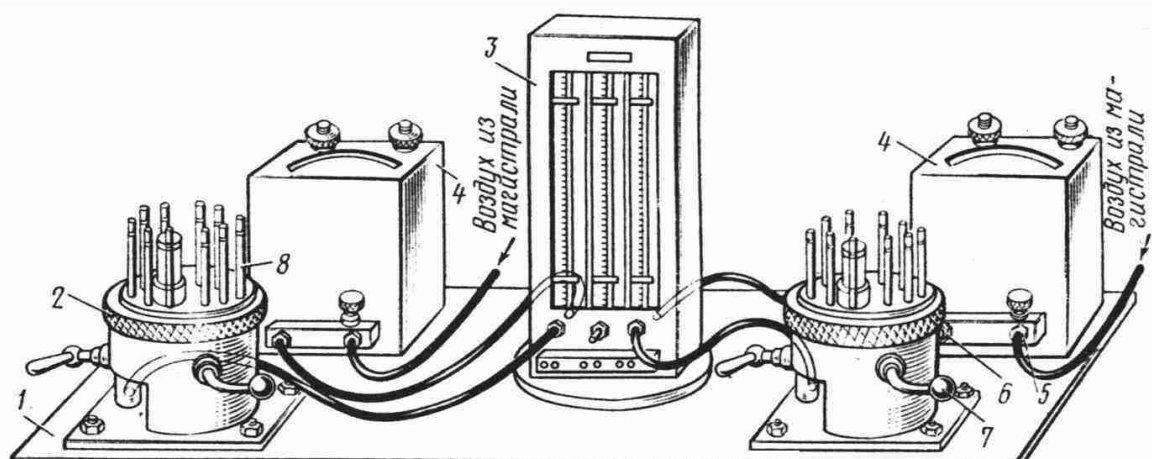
Стенд для измерения отверстий корпуса распылителя и гильзы плунжера
